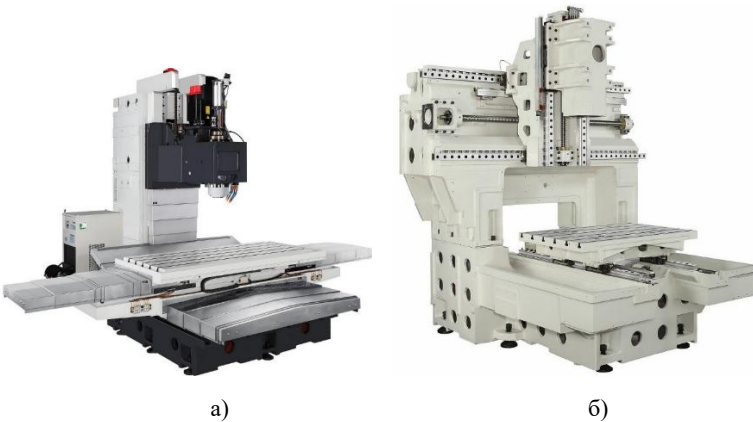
Компонування 3-осьових фрезерних верстатів: а – з хрестовим столом; б – порталне
